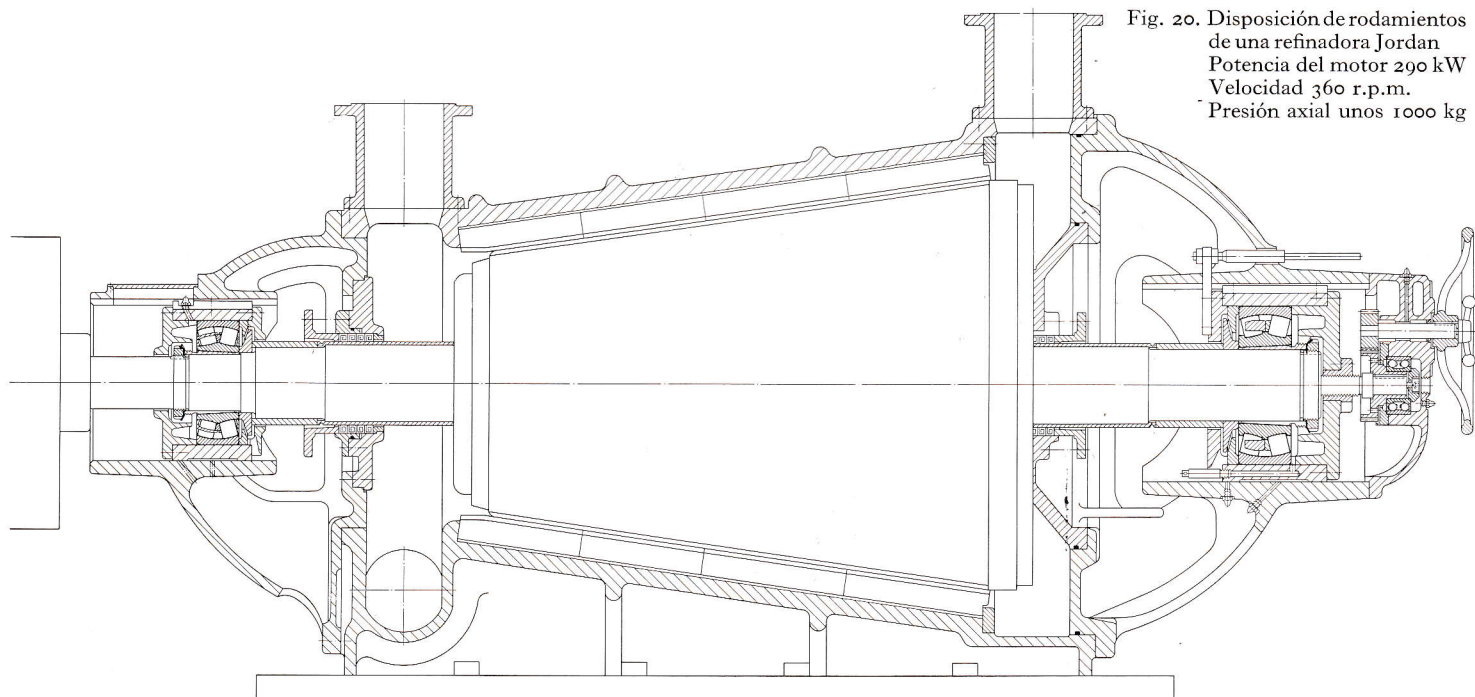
Disposición de rodamientos de una refinadora Jordan
